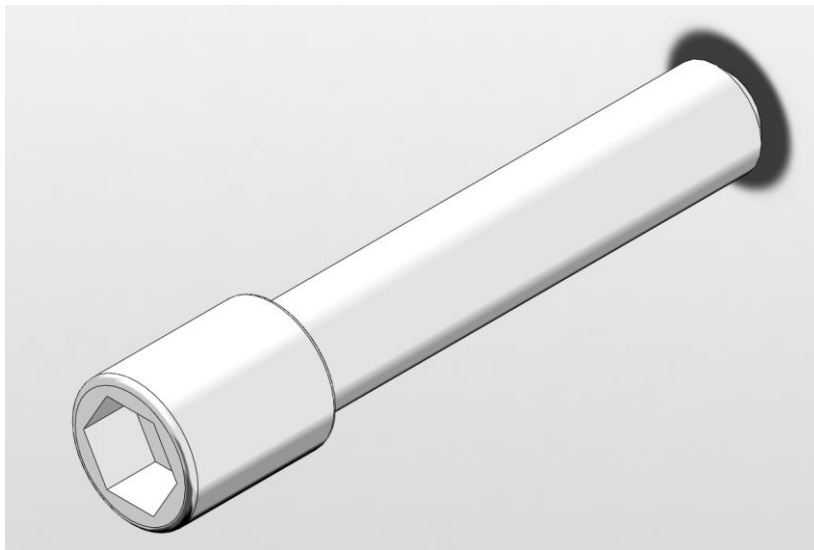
Imagen 3D de la pieza tornillo pequeño.
